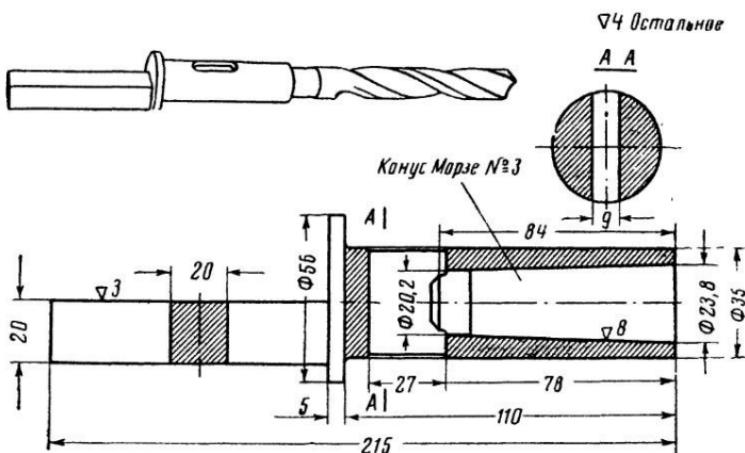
Приспособление для закрепления сверл в резцодержателе.
